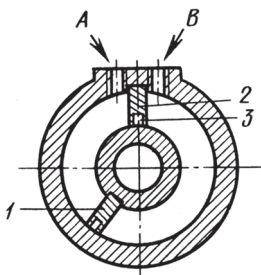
Схема пластинчатого (лопастного) поворотного двигателя
